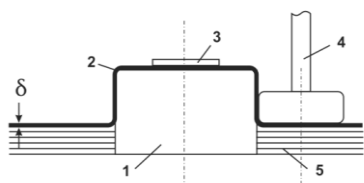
Схема ротационной обкатки при неподвижной заготовке:
